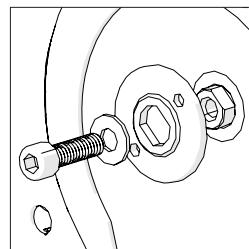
Fahren Sie anschließend mit dem Entfernen der Spindelschraube, Unterlegscheibe und dem äußeren Sägeblattflansch fort. (Abb. 27)
